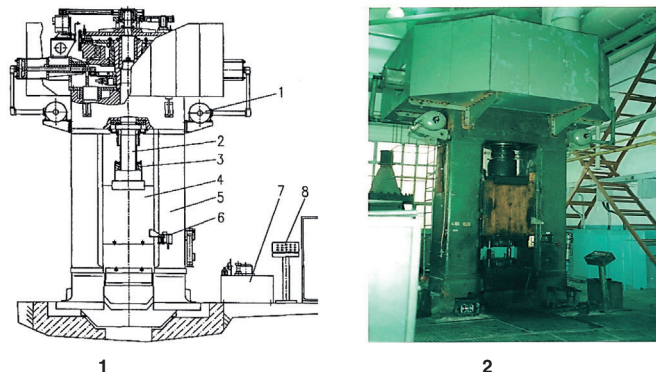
Винтовой пресс с муфтовым приводом Ф1738М силой 6300 кН: 1 — схема пресса: 1 — ресиверы; 2 — винт; 3 — гайка; 4 — ползун; 5 — направляющие станины пресса; 6 — конечный выключатель; 7 — система смазки; 8 — пульт управления; 2 — общий вид пресса
